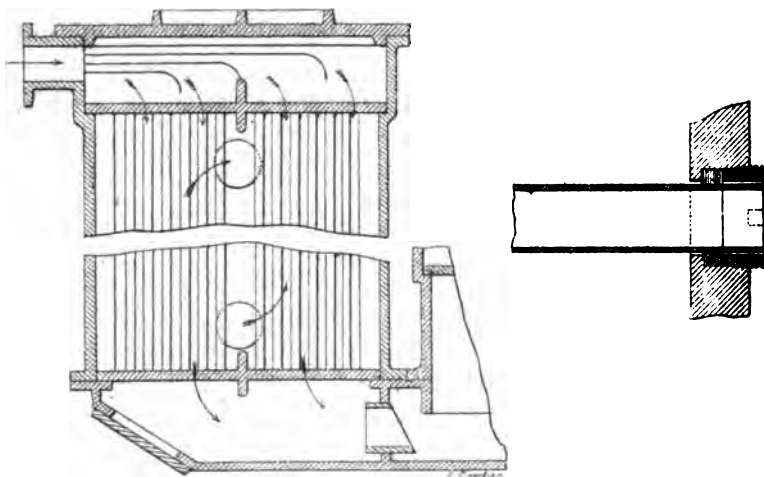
Condenseur à surface de Hall pour machine marine (1835).
